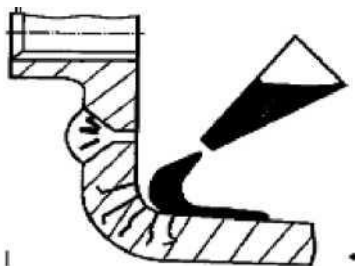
Схема просочування для усунення мікропор зварних швів і мікротріщин деталей
